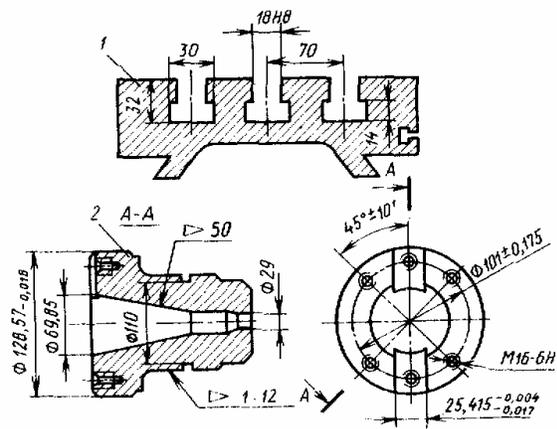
Установочные базы горизонтально-фрезерного станка 6Р83Г (1 – пазы стола; 2 – шпиндель)
